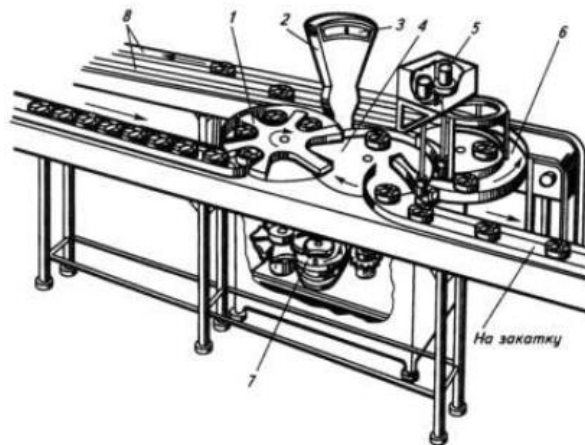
Автомат для контролю маси наповнених консервних банок: 1 - приймально-подавальна зірочка; 2 - циферблатні ваги; 3 - фотоелектрична шкала ваг; 4 - диск, що обертається; 5 - розподільний пристрій; 6- стіл, що обертається, подачі банок з відхиленнями від заданої маси; 7 синхронізує пристрій; 8 конвеєр повернення банок з відхиленнями від заданої маси
